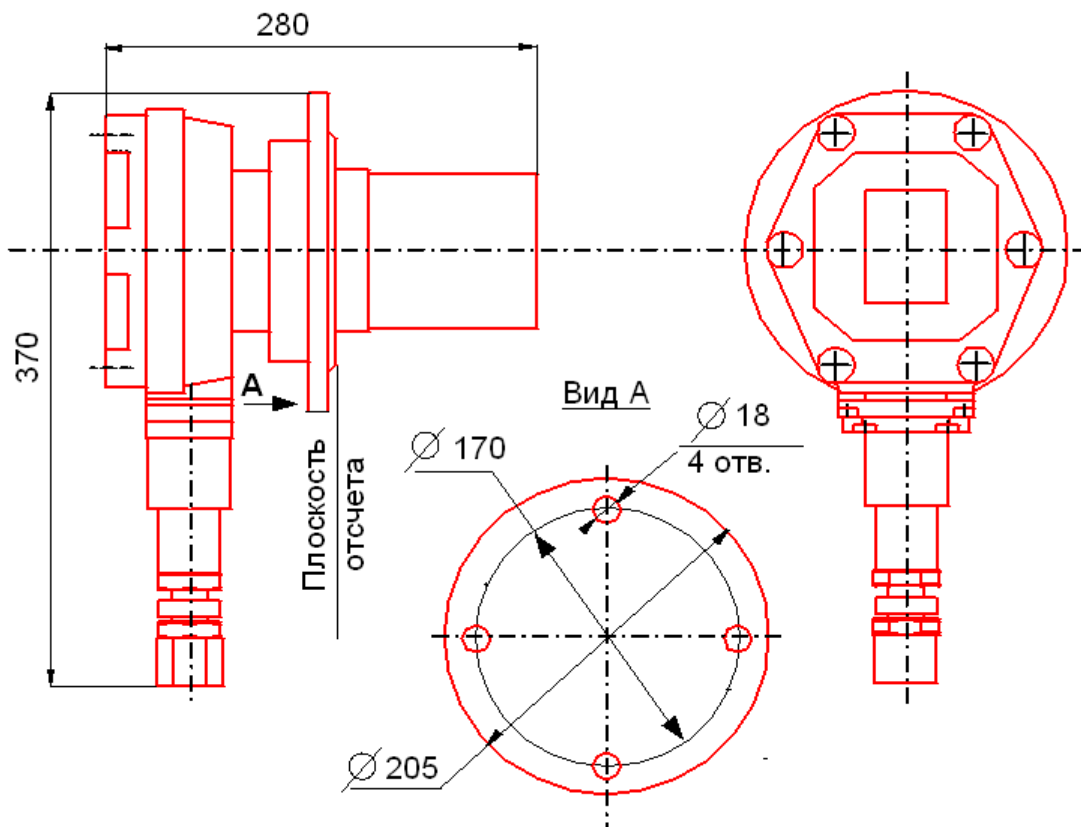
Габаритные и установочные размеры акустического преобразователя АП-61В
